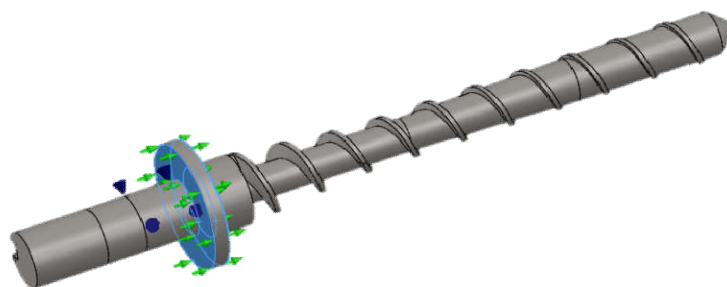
Fixações e restrições aplicadas ao fuso (estudo 1)
